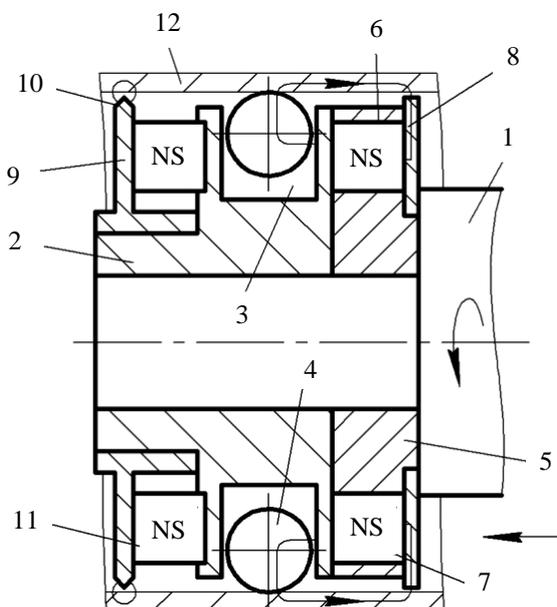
Конструкция инструмента для СМДН цилиндрических поверхностей с устройством улавливания ферромагнитных частиц
